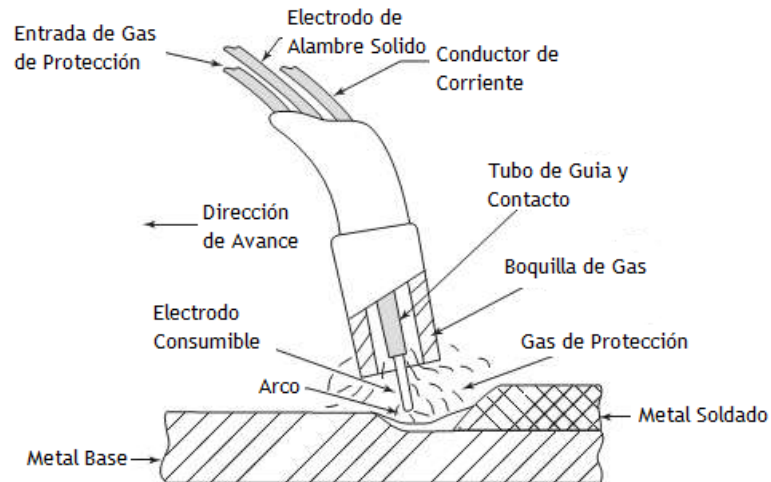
Partes del Proceso GMAW. Gas Metal Arc Welding.
